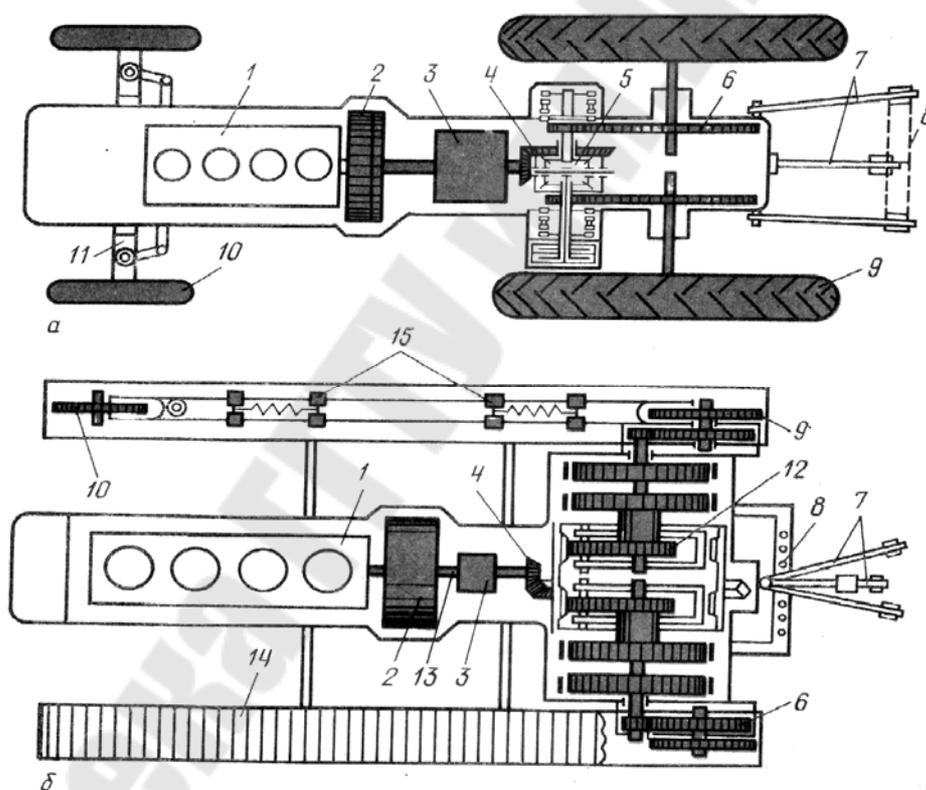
Схемы расположения основных механизмов тракторов: А – МТЗ-80; б – ДТ-75-МВ; 1 – двигатель, 2 – сцепление, 3 – коробка передач, 4 – главная передача, 5 – дифференциал, 6 – конечная передача, 7 – навесное устройство гидросистемы, 8 – прицепное устройство, 9 – ведущее колесо, 10 – направляющее колесо, 11 – передний мост, 12 – планетарный механизм, 13 – соединительный вал, 14 – гусеничная цепь, 15 – каретка подвески.
